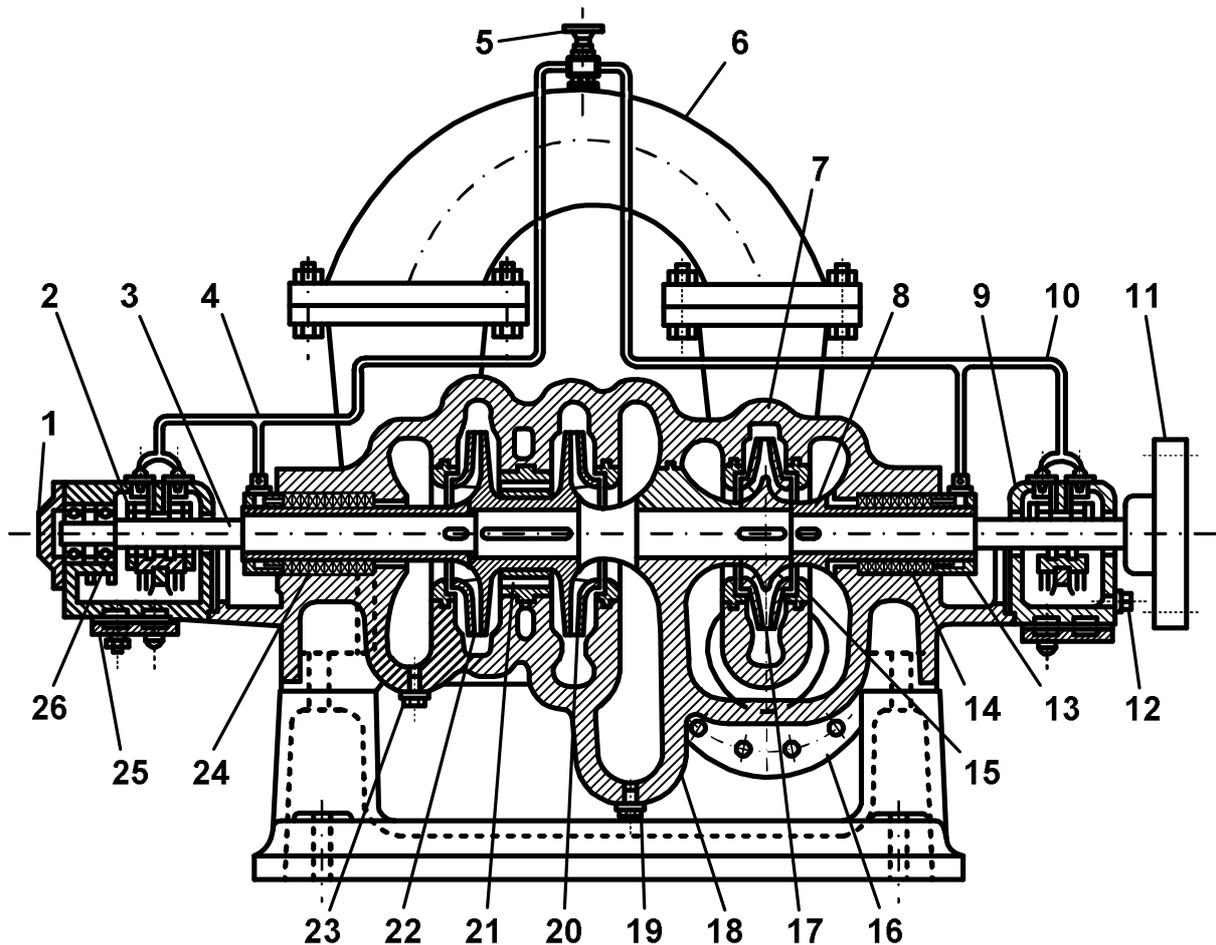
Спиральный насос типа МД:1 – глухая крышка; 2 – подшипник скольжения; 3 – вал; 4 и 10 – подвод воды на гидрозатвор сальника и подшипники; 5 – распределительный кран; 6 – обводная труба; 7 и 18 – верхняя и нижняя части корпуса насоса; 8 – защитная втулка сальника; 9 и 25 – корпус передней и задней подшипниковой опоры; 11 – полумуфта; 12 – пробка для слива масла; 13 – фланец сальника; 14 и 24 – сальники передний и задний; 15 – уплотняющие кольца; 16 – всасывающий патрубок; 17 – рабочее колесо 1-й ступени; 19 и 23 – нижняя и верхняя пробки корпуса; 20 и 22 – рабочие колеса 3-й и 2-й ступени; 21 – разгрузочная втулка; 26 – радиально-упорный подшипник
